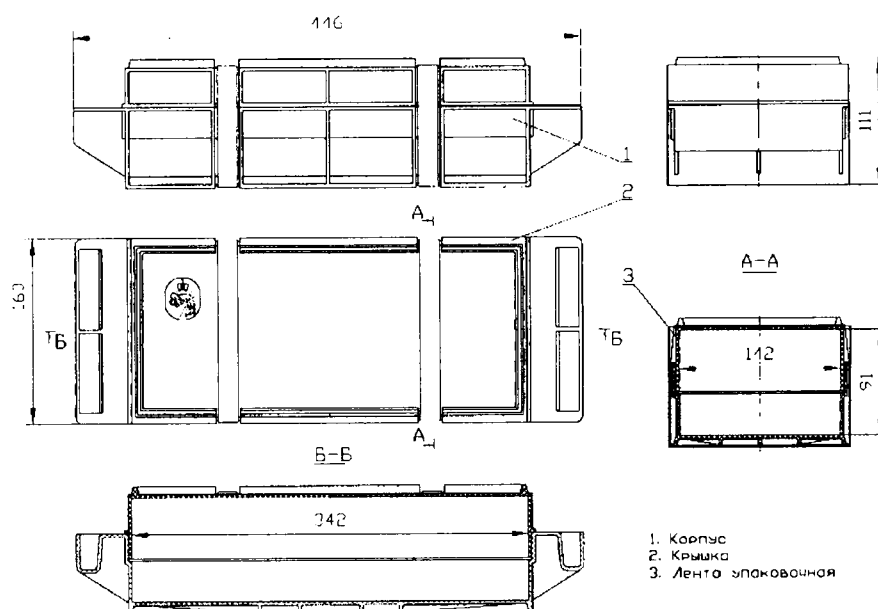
Сборочный чертеж контейнера КТ-1С
